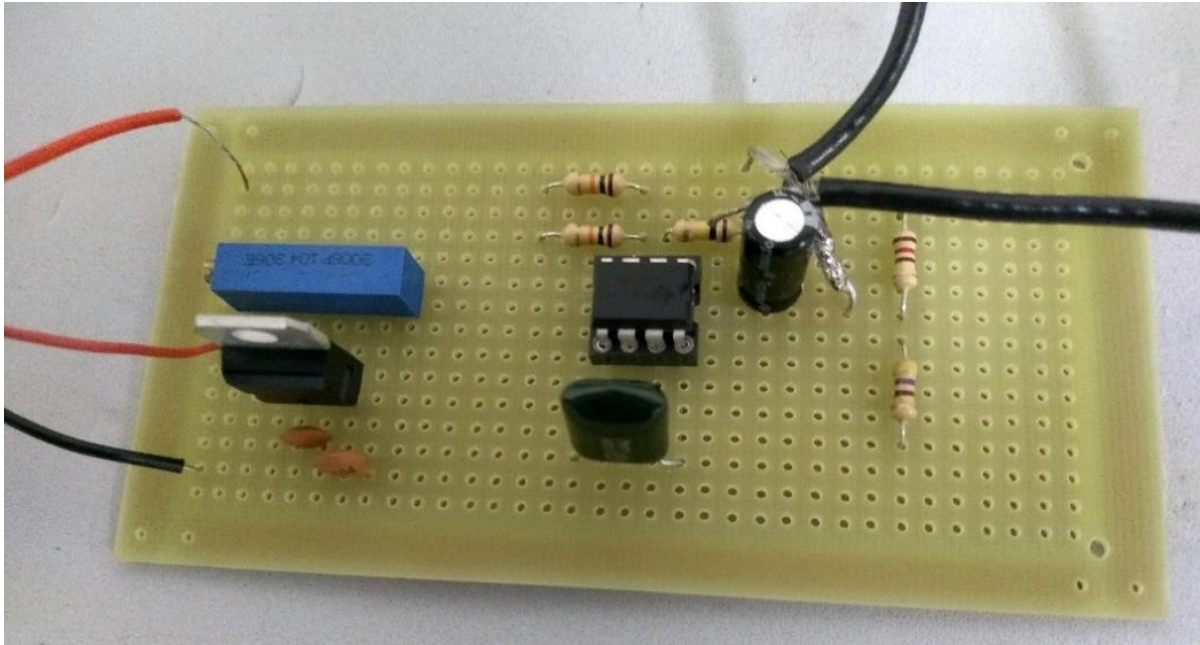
Protótipo de componentes montado e soldado em uma placa de fenolite perfurada.
